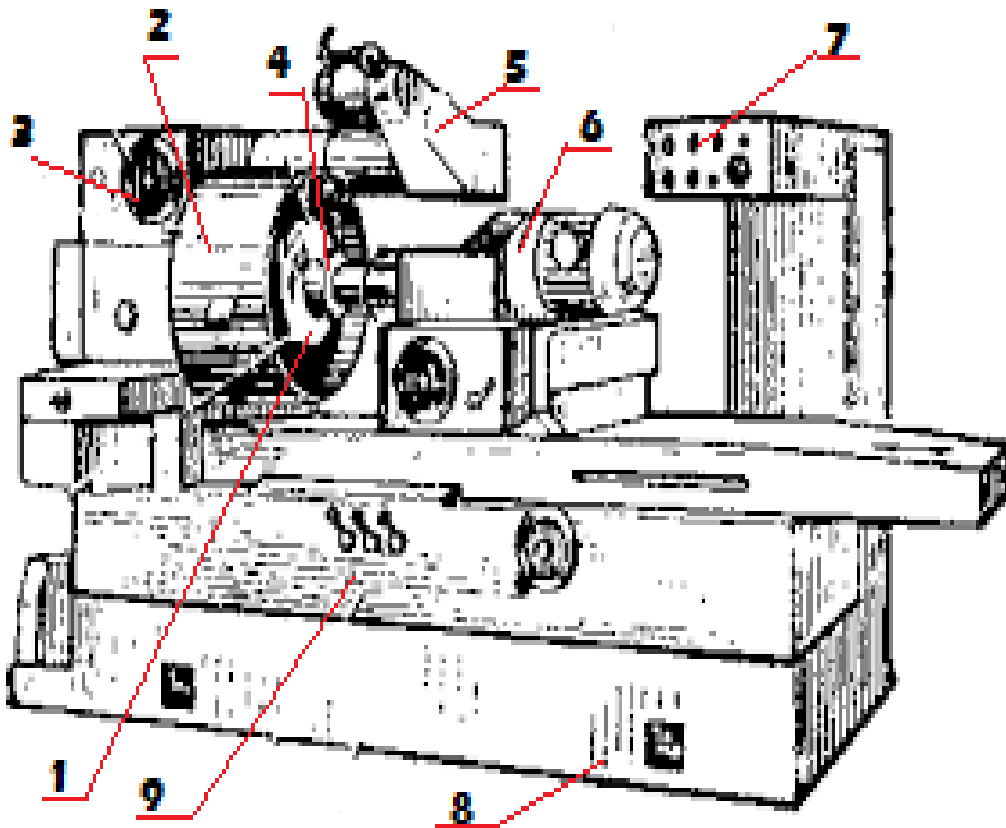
Зовнішній вигляд внутрішньо-шліфувального верстата[2]:
